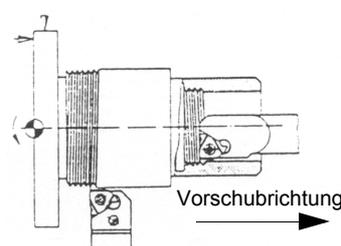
Linksgewinde bei Rechtslauf der Maschinenspindel
